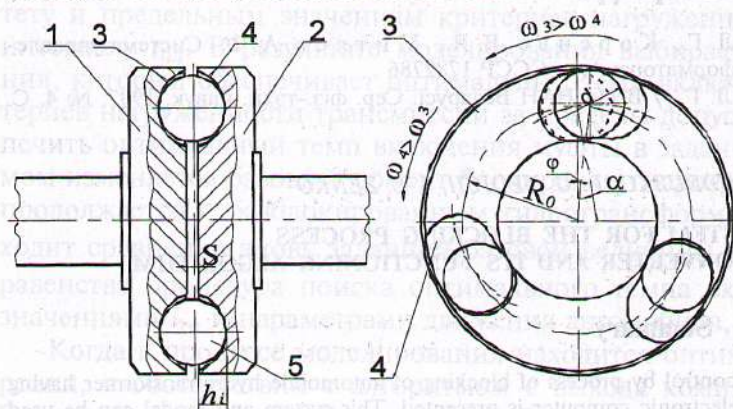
Схема конструкции шарикового механизма свободного хода торцового типа (А. с. 1756684): 1, 2 — ведущая и ведомые полумуфты; 3 — концентричная канавка; 4 — дугообразный паз; 5 — шарик; α — угол заклинивания; φ — угол относительного поворота полумуфт при заклинивании
